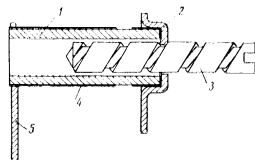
Цилиндрический плунжерный подстроечный конденсатор
